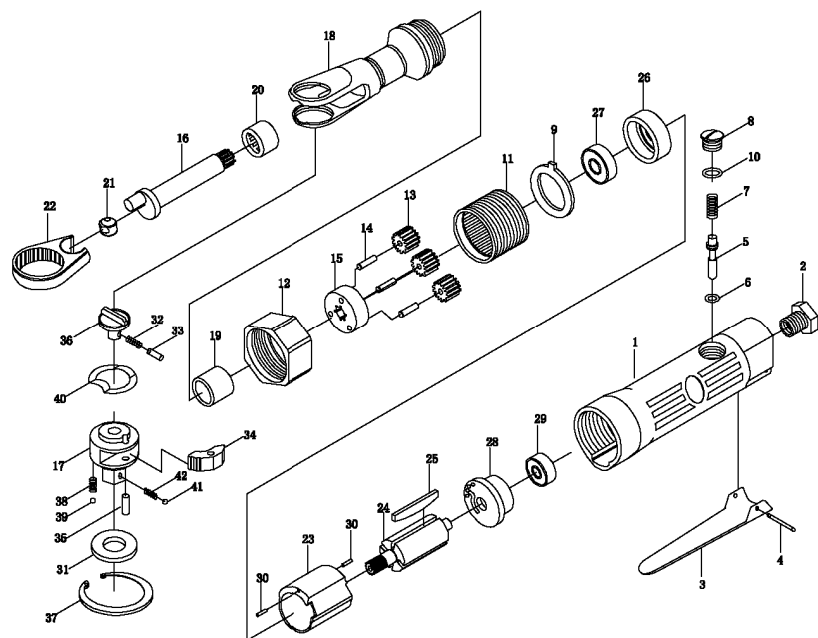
Принципиальное устройство и схема сборки трещоточного гайковерта
